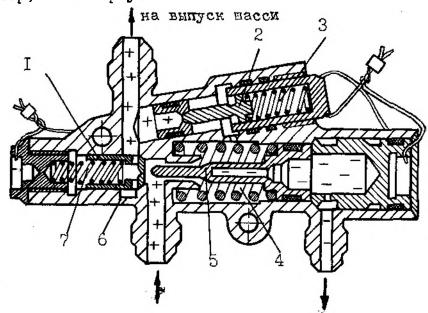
Гидрозамок шасси клапан; 2 - термоклапан; 3,4,7 - пружина; 5 - поршень со штоком; 6 - корпус
